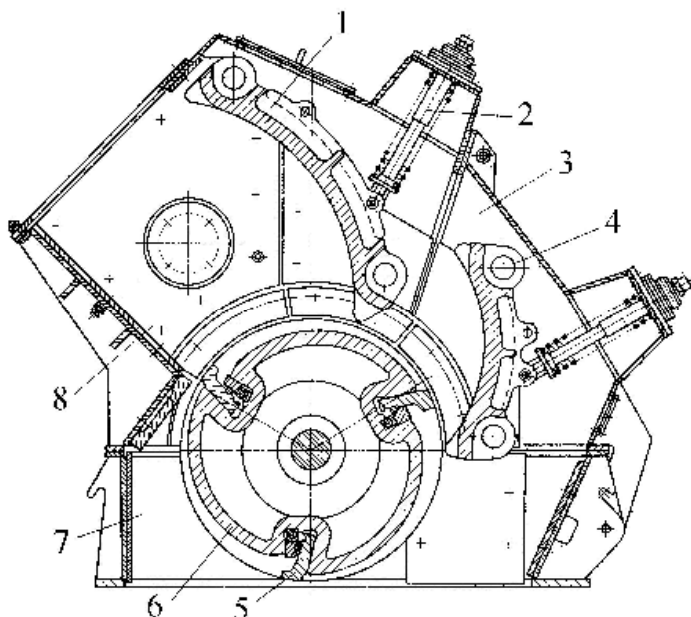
Однороторная дробилка крупного дробления СМД-86А
